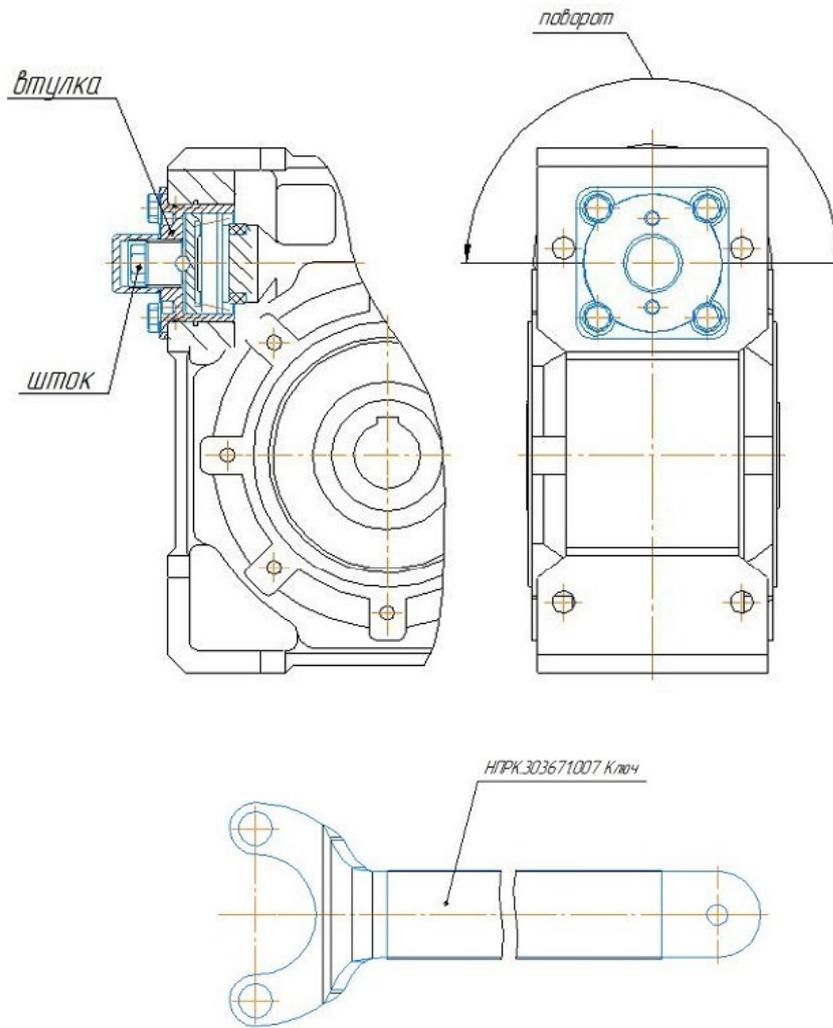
Выборка осевого люфта червячного вала редуктора
